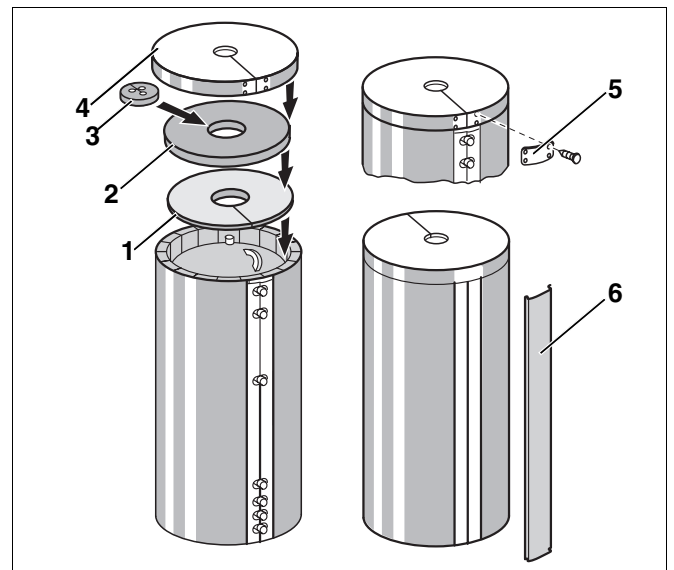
Montage Wärmeschutz (Prinzipdarstellung)
